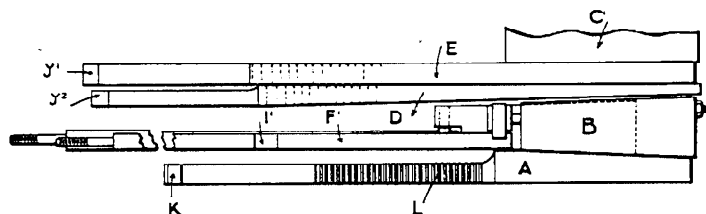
ENSEMBLE DES DIVERS COINS, VUS EN PLAN.
